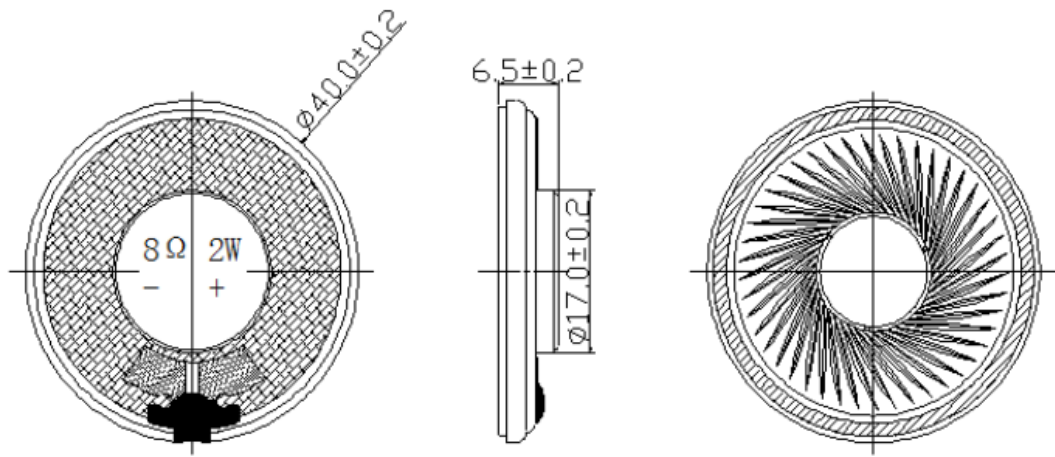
Габаритні розміри гучномовця UG-40008F-162R
